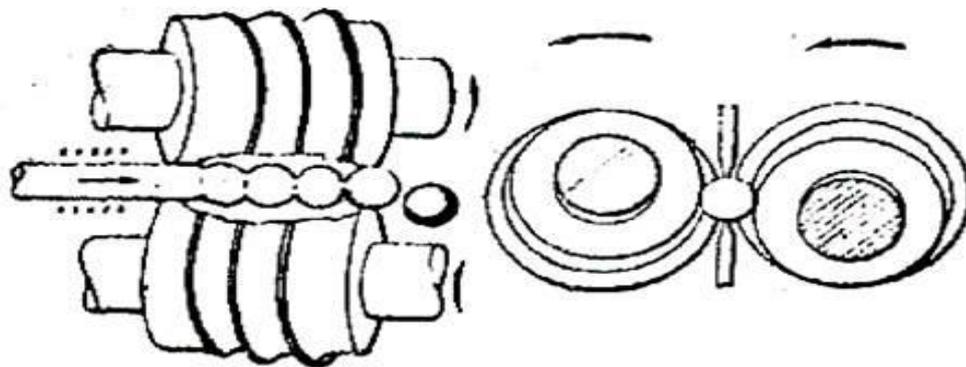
Схема прокатки шаров в винтовых калибрах
